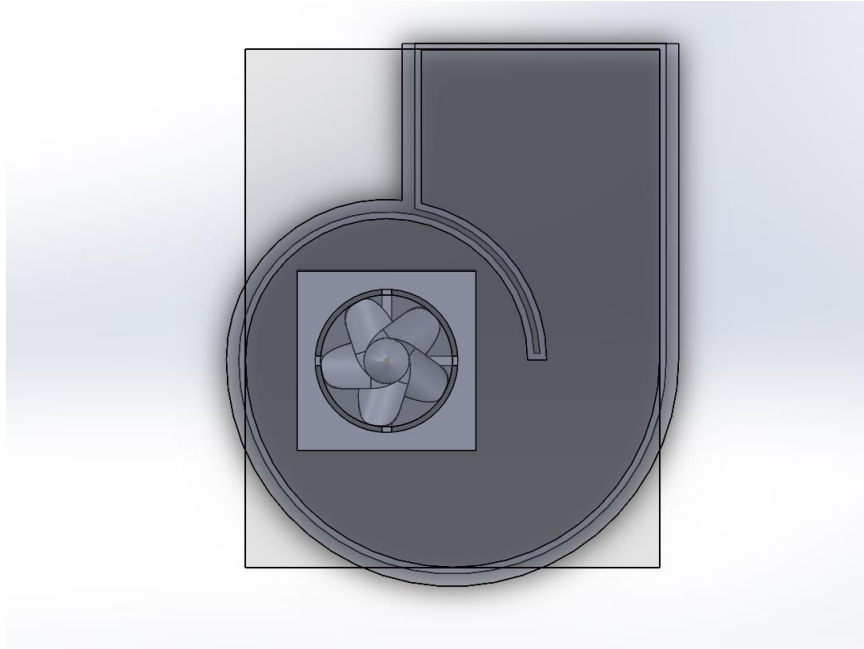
Vista superior de ensamble considerando las tres partes principales (Estructura metálica, obra civil y turbina Kaplan)
